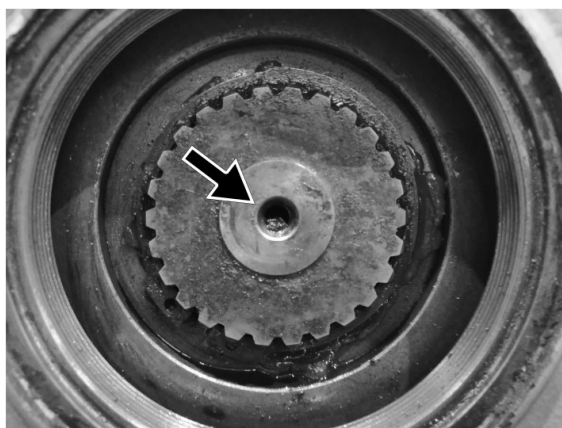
Резьбовое отверстие в шлицевом вале
